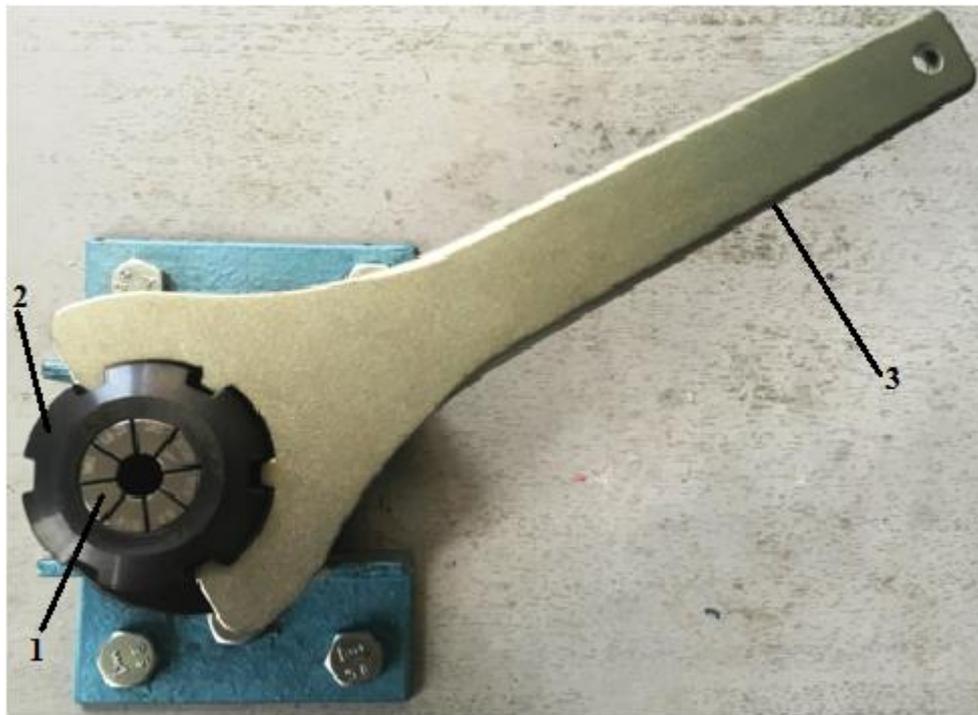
Затяжка гайки цангового патрона: 1 - цанга; 2 - гайка ; 3 - ключ.
